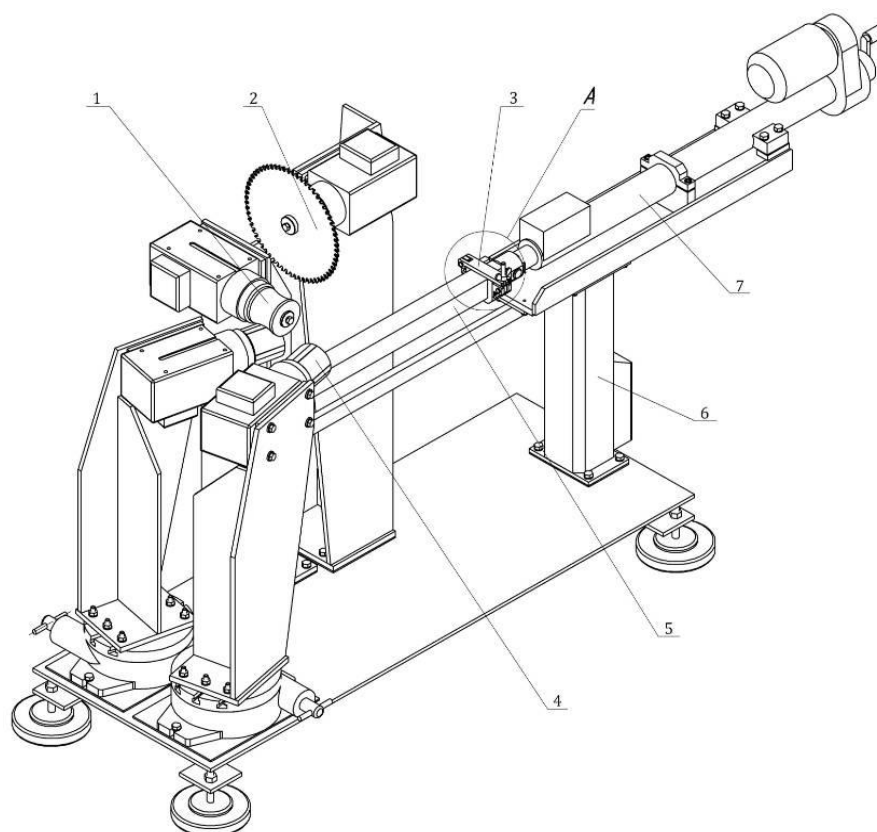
Общий вид станка для нарезки секторов ШНС-03:
